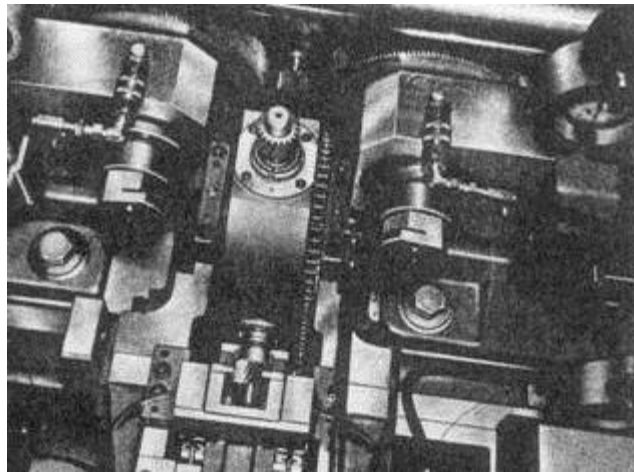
Laminadora automática de engranes con mecanismo de torreta para carga y descarga de las preformas.
